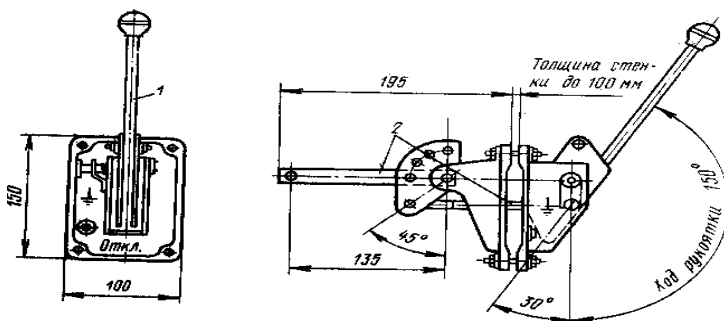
Ручной рычажный привод ПР -10 для управления разъединителем 1 – рукоятка; 2 – система тяг и рычагов
